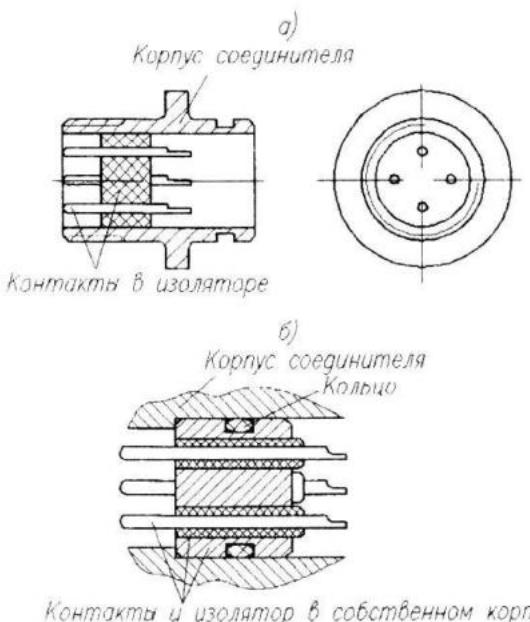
Блоки контактов (а - в корпусе соединителя; б - в собственном корпусе).
